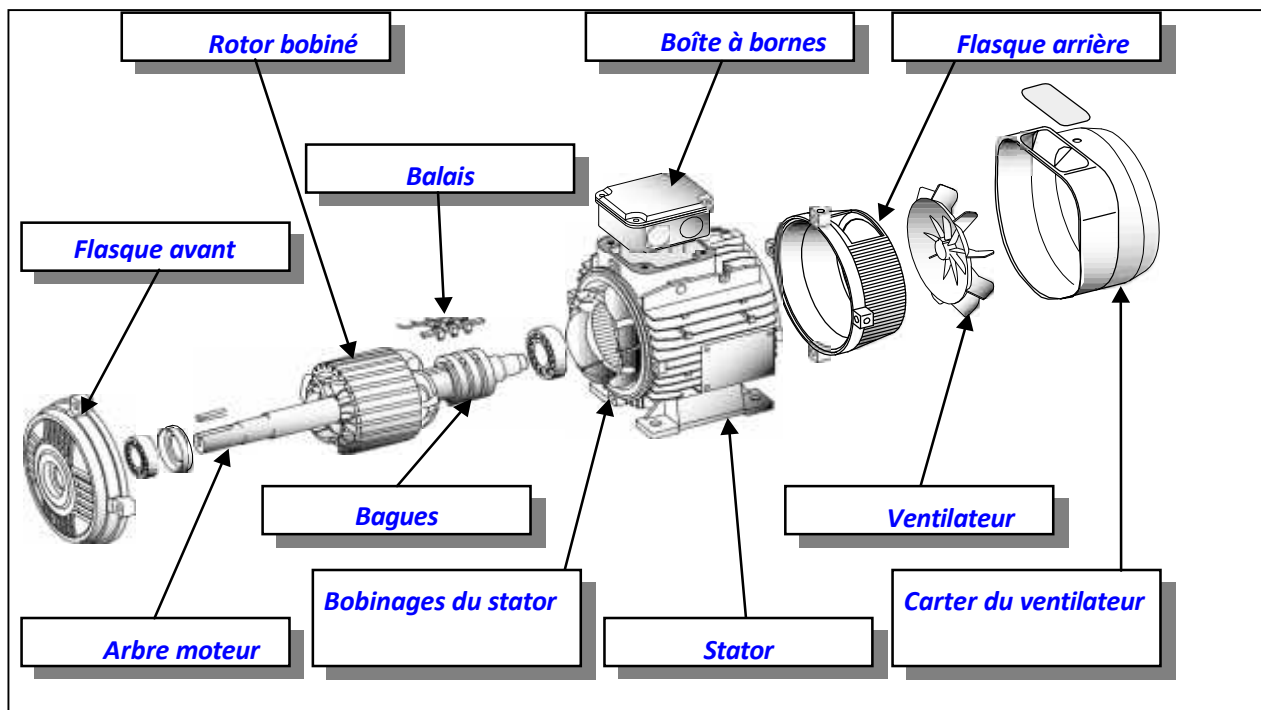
Vue éclatée d'un moteur asynchrone rotor à bagues.
